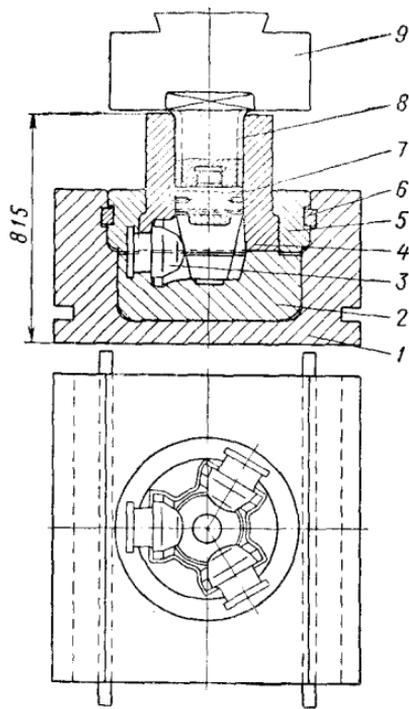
Штамп с разъемной матрицей для поковки втулки трехлопастного винта:
